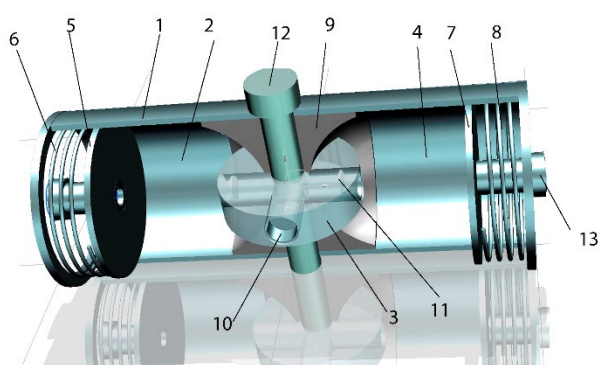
Схема некоторой гипотетической установки, имитирующей «холодильный цикл». 1 – корпус; 2 – полость холодного потока; 3 – крестовина с цилиндрами и с поршнями; 4 – полость горячего потока; 5 и 7 – поршни; 6 и 8 – пружины; 9 – вставка; 10 – цилиндрик-микровихрь; 11 – поршень цилиндрика; 12 –
